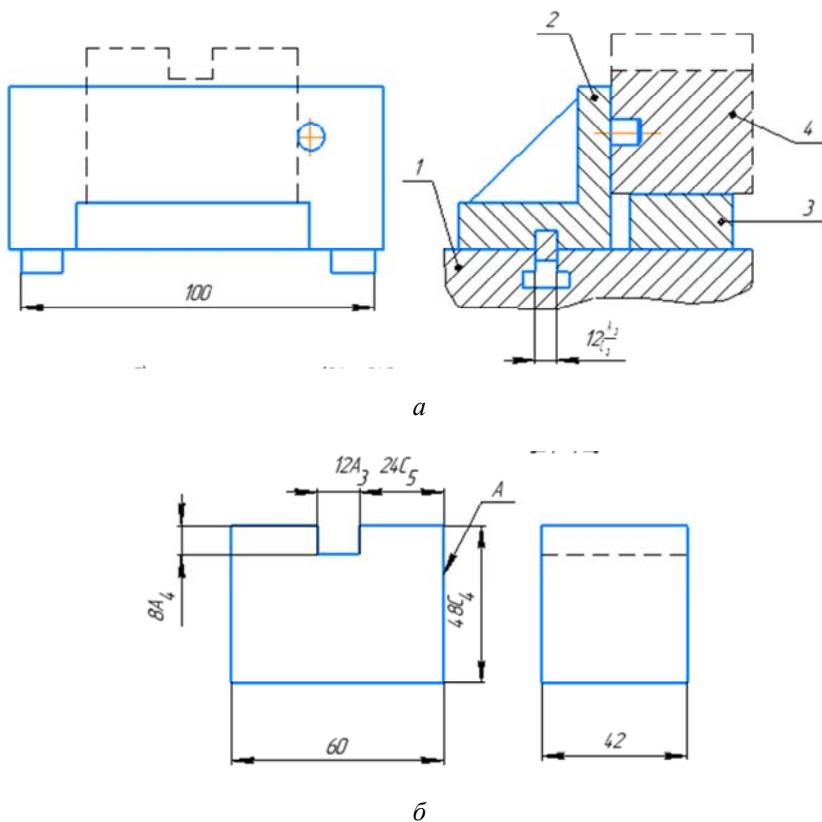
Схема установки детали в гидравлических тисках с наладкой (а) и обрабатываемая модель (б):
